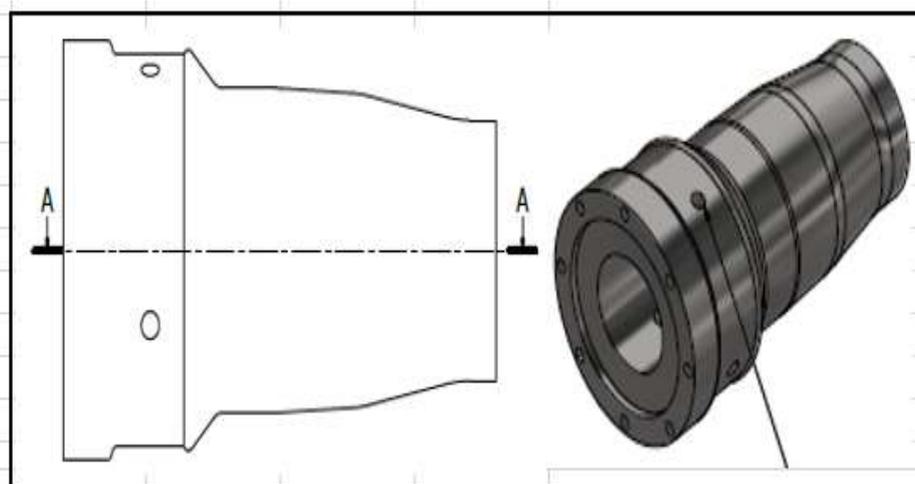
PARTE 3 DE NUEVA BOQUILLA
